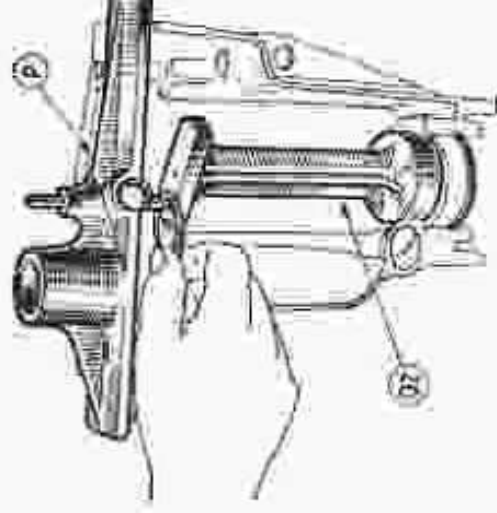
Mesure de l'épaisseur de la cale à monter.
